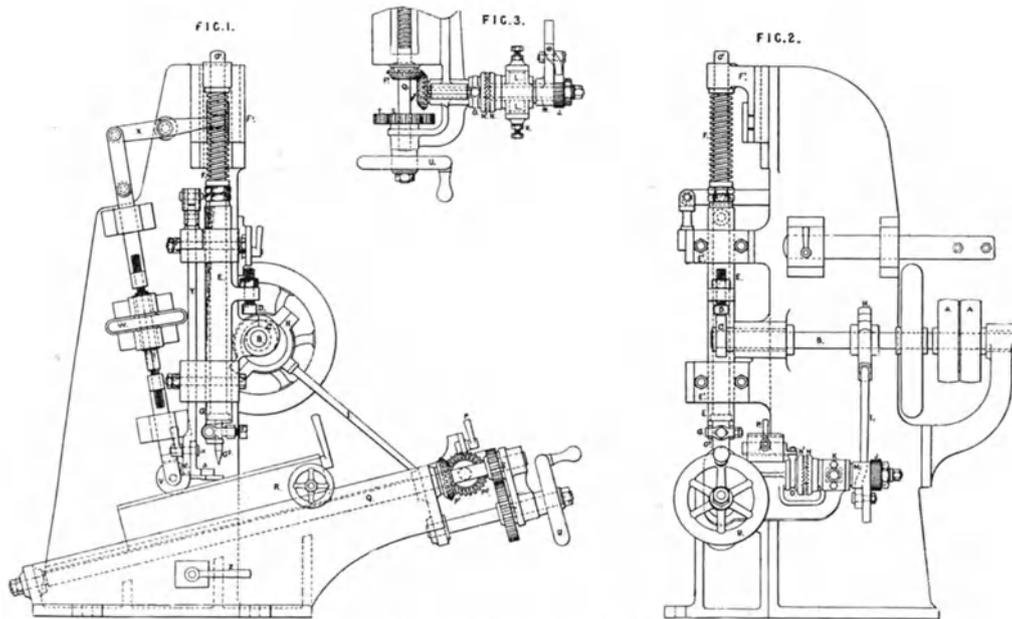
Englische Haumaschine „Shardlow“ 1883.
